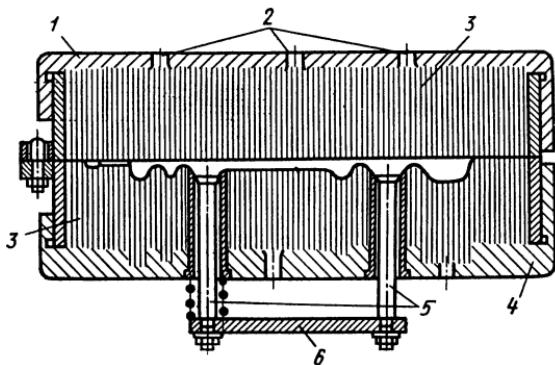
Податливый и газопроницаемый кокиль, собран-
